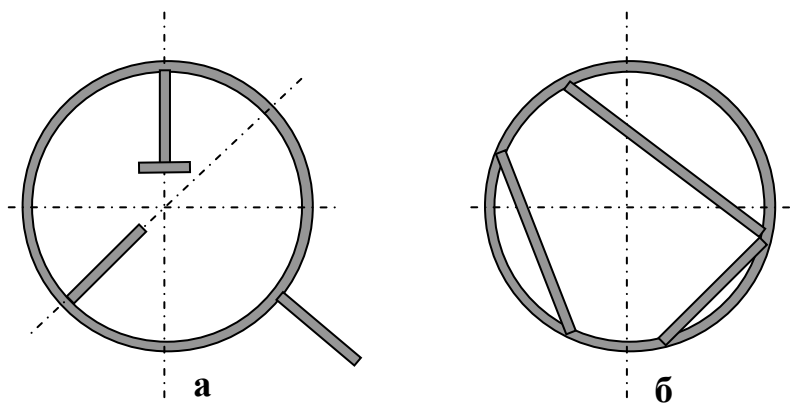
Схема розміщення пластин (поперечний переріз оболонки)
